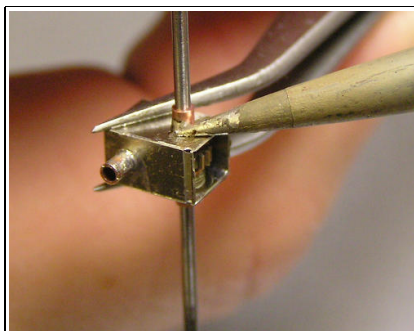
Die Buchse verlöten und das Getriebe wieder zerlegen.
